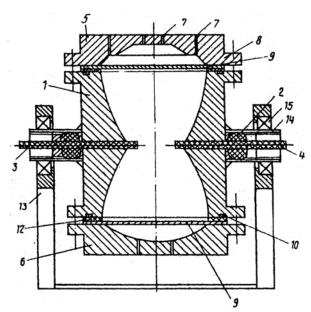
Рабочая камера для электрогидравлической штамповки (вид спереди)
